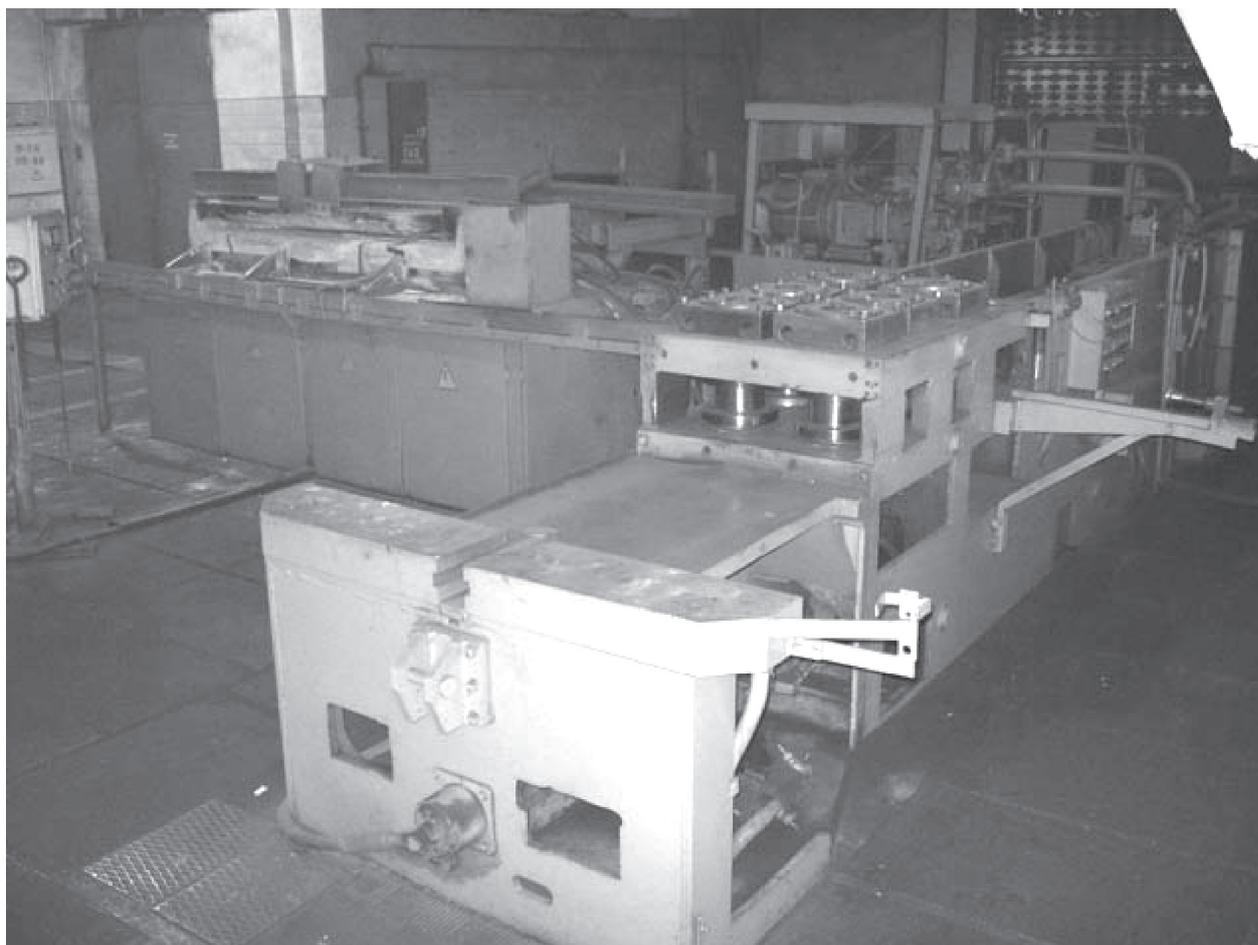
Стан СП-1298М для прокатки заготовок прорессорника
